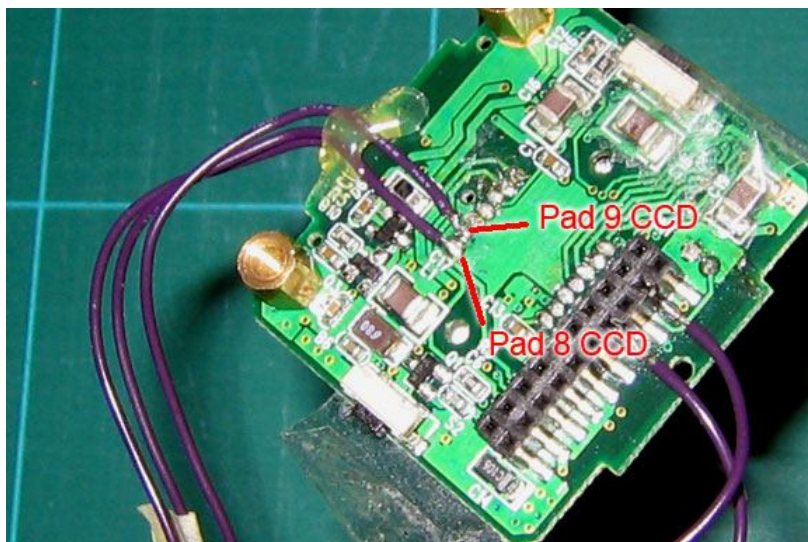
Detalle de los cables soldados a los puntos Pad 8 y 9 del CCD
